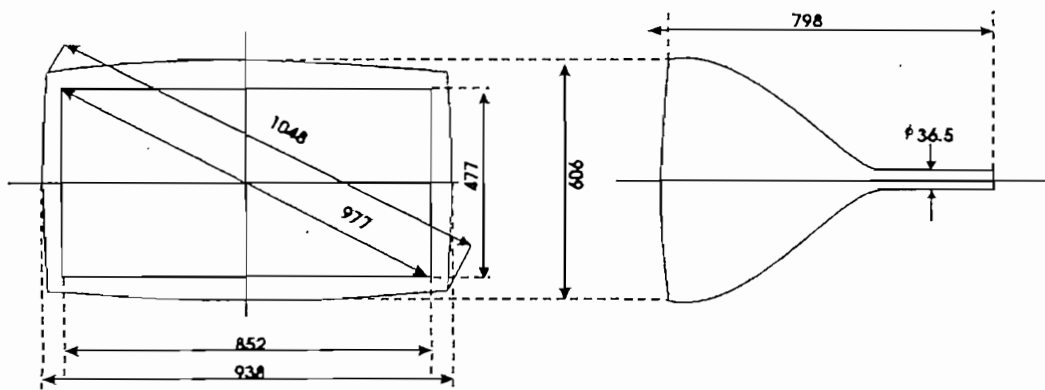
1 Dimensiones del TRC de 38" (en mm.).
